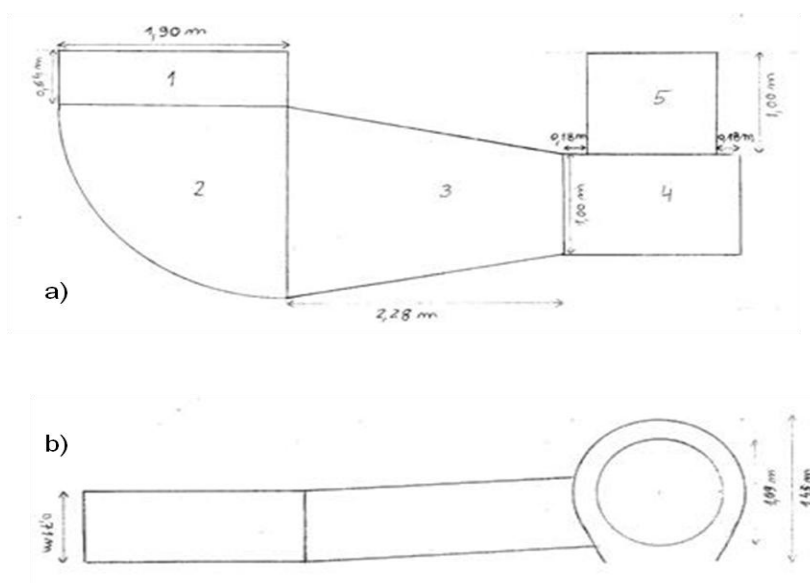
Ventilador de recirculação das estufas a) vista de cima b) vista frontal
